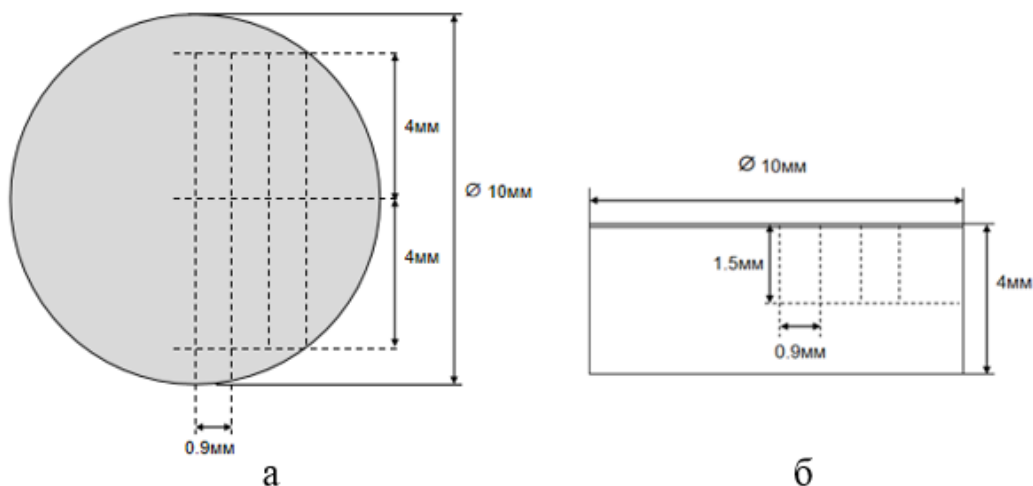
Схематическое изображение вырезки заготовок из исследуемых образцов: а – вид сверху; б – поперечное сечение
